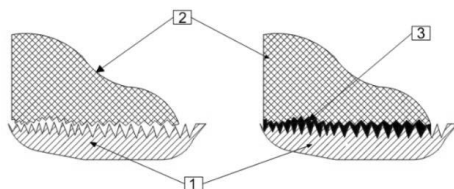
Контакт опорних поверхонь оправки та ріжучої пластини:
